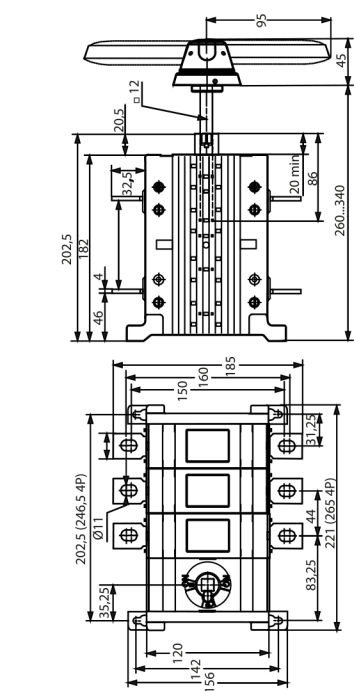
Габаритные и установочные размеры реверсивных рубильников 315-400А
